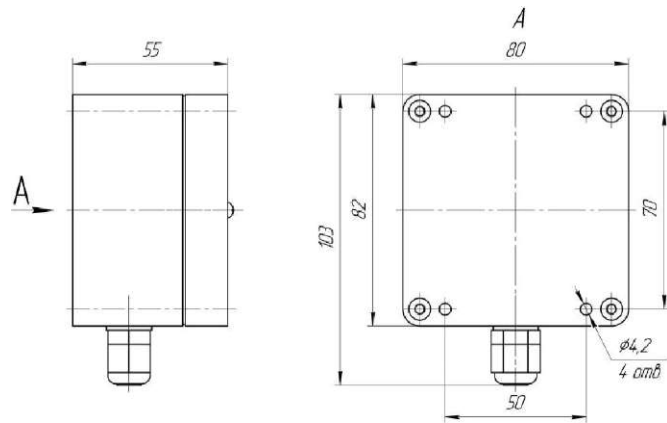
Габаритные и присоединительные размеры датчика ДГС ЭРИС-220.
